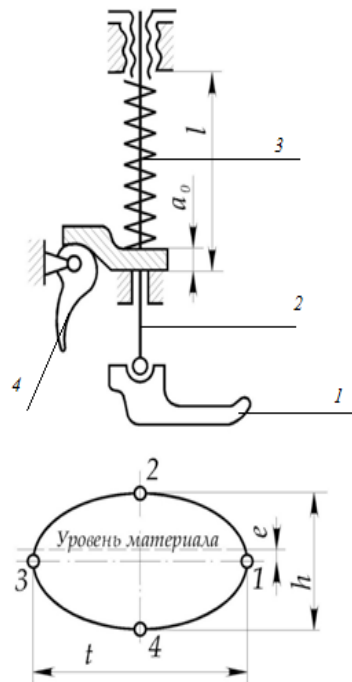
Схема механизма прижимной лапки и траектория зубчатой рейки: 1 — лапка; 2 — стержень; 3 — пружина; 4 — регулятор подъема лапки
